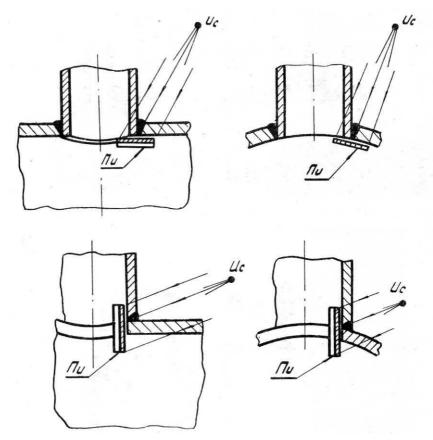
Схема просвечивания швов врезки снаружи трубы за несколько установок источника излучения
